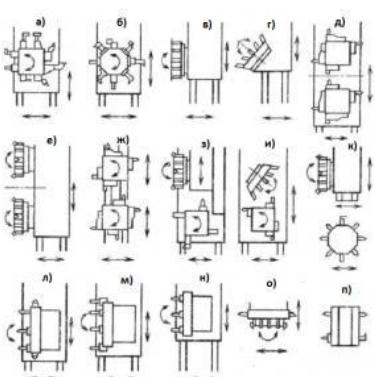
Схемы конструктивного исполнения револьверных головок токарных станков
